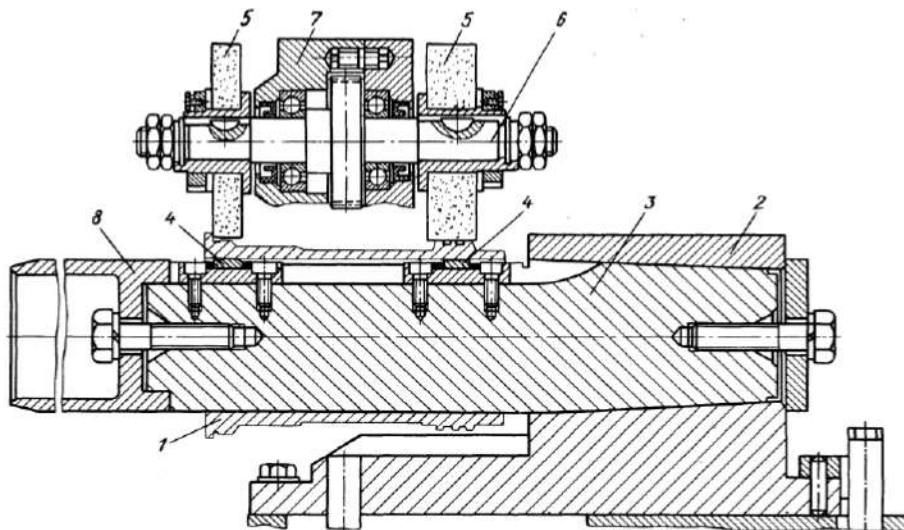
Приспособление для шлифования на жестких опорах:
